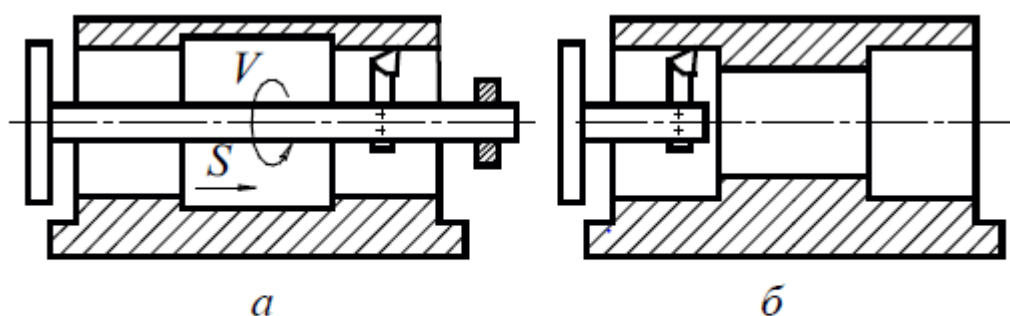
Конструкция корпусных деталей с соосными отверстиями:
